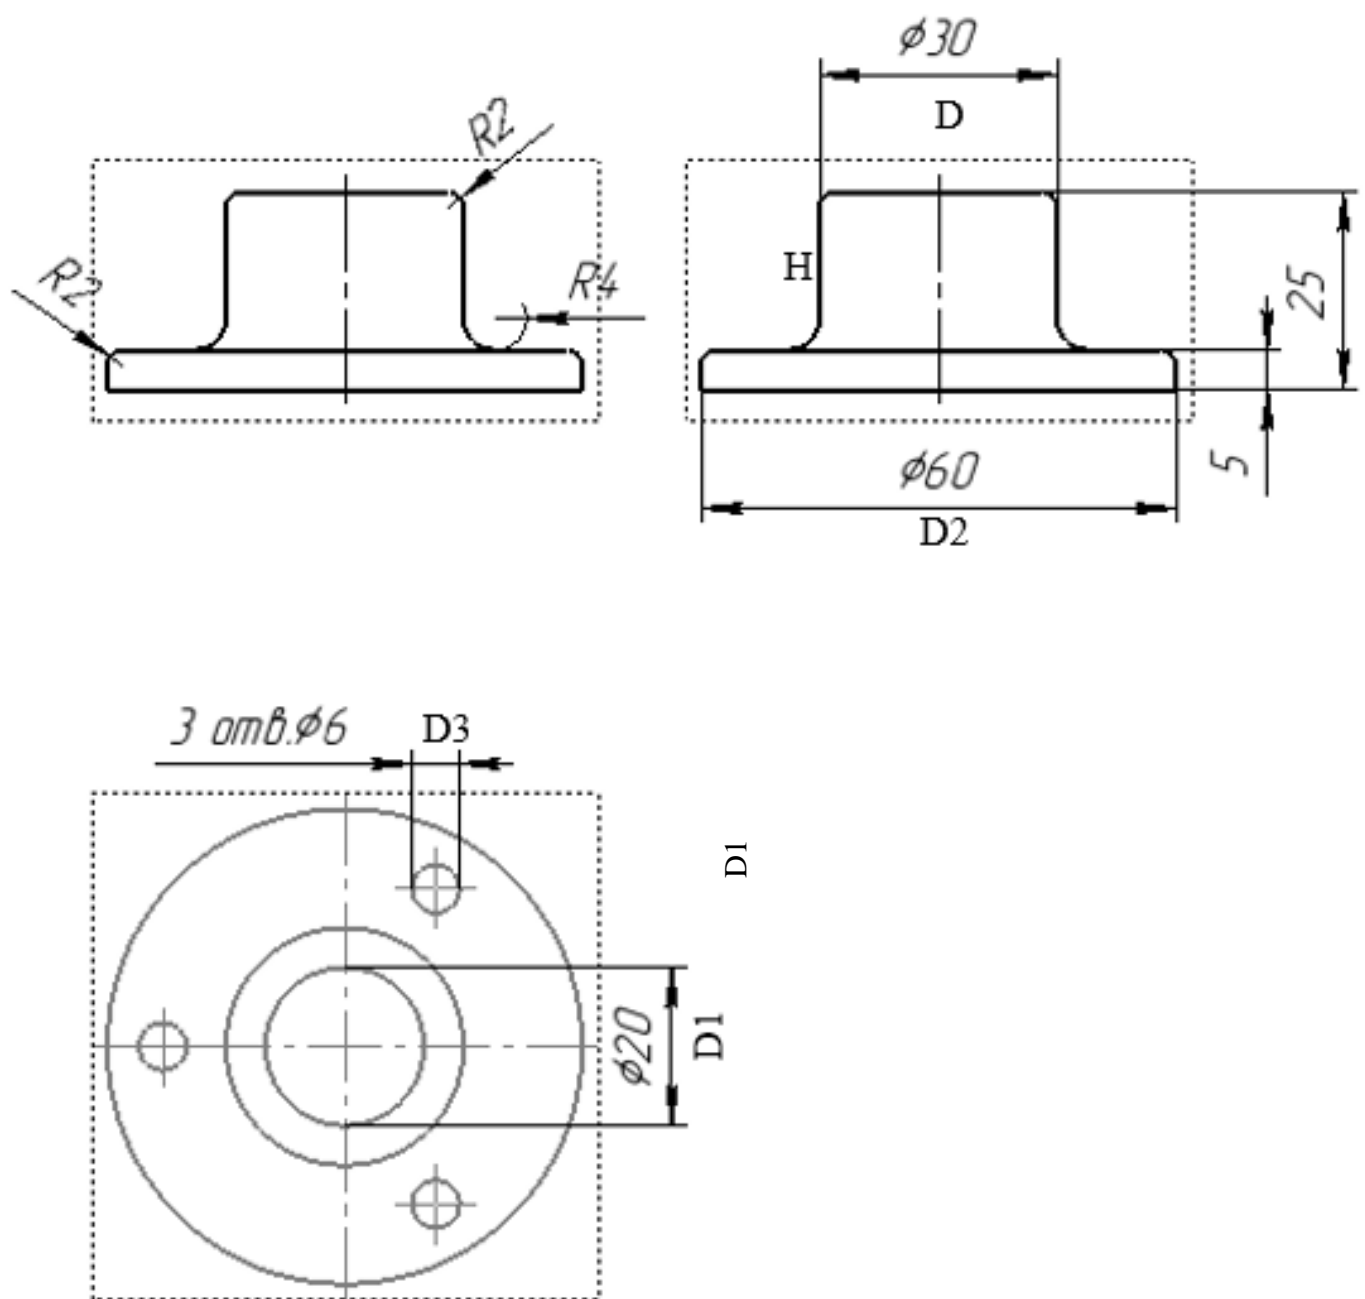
Чертеж модели держатель для крепления трубы к стене
